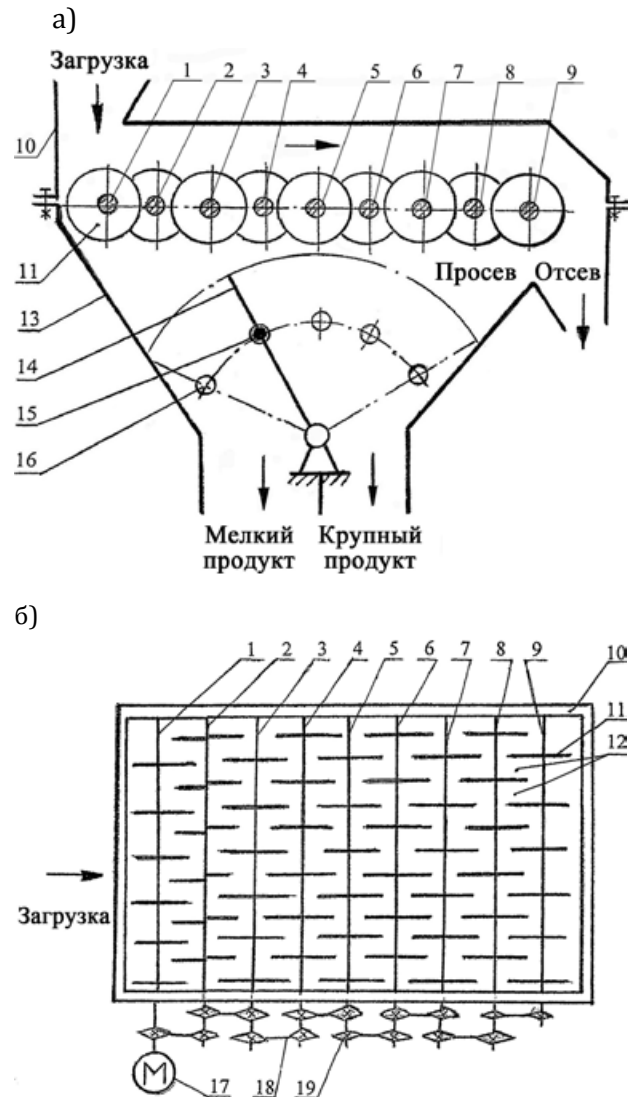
Схема опытно-промышленного валково-дискового грохота: 1–9 – валы; 10 – корпус; 11 – диски; 12 – ячейки; 13 – бункер; 14 – дроссельная заслонка; 15 – задвижка; 16 – отверстия под задвижку; 17 – привод; 18 – цепные передачи; 19 – звездочки
